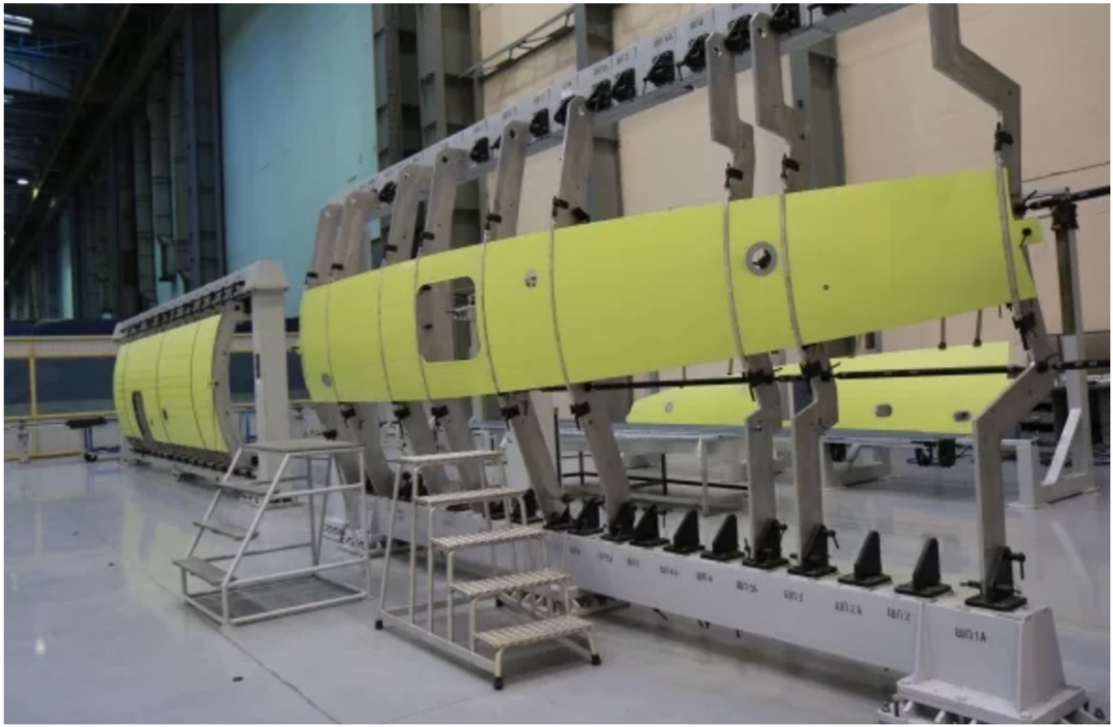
Сборочное приспособление для изготовления панели фюзеляжа
